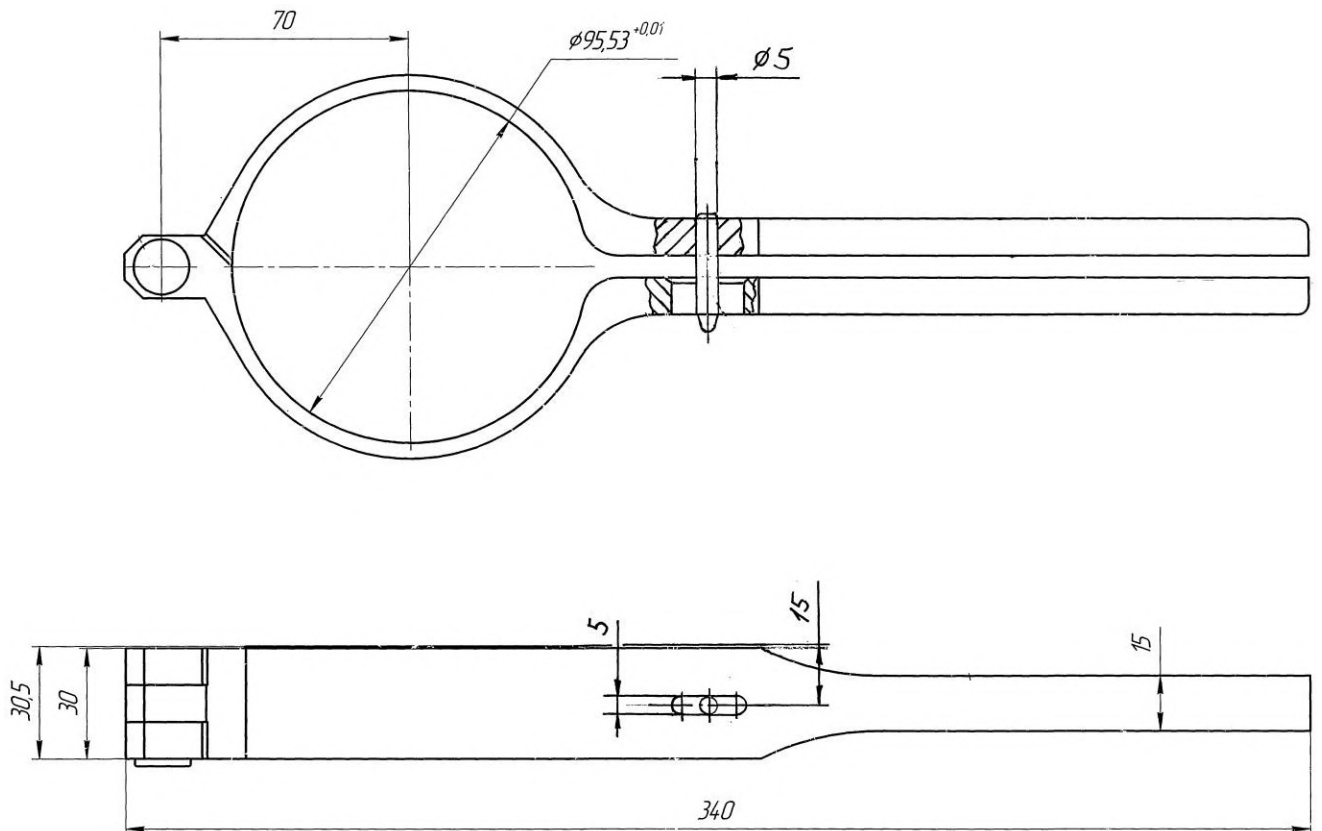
ZM 7820-4517 – Spannvorrichtung zum Zusammendrücken von Kolbenringen $\varnothing 95,5$ mm
